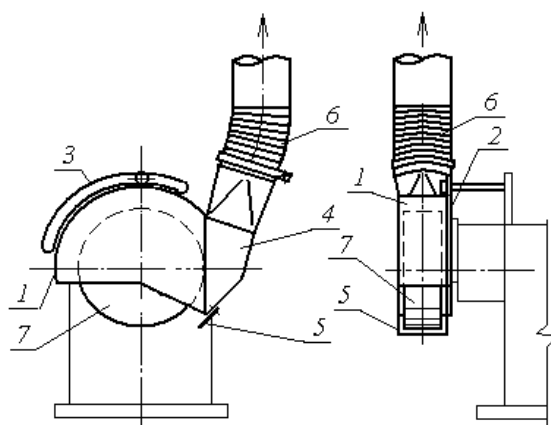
Защитно-обеспыливающий кожух универсально-заточного станка
